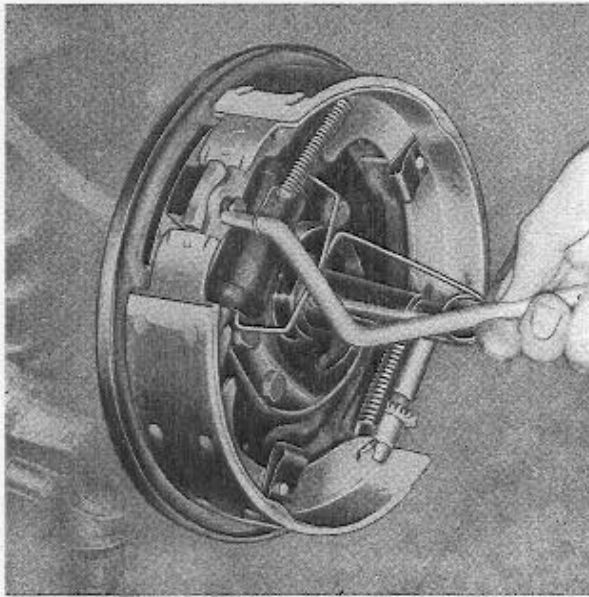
Einbau der Rückhofeder mit Bremsfederwerkzeug
